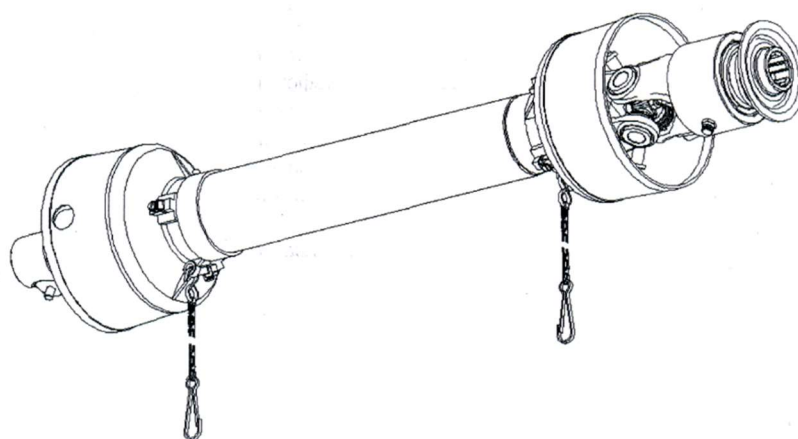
Конструкция карданного вала АК-40.016.3000-065/098
